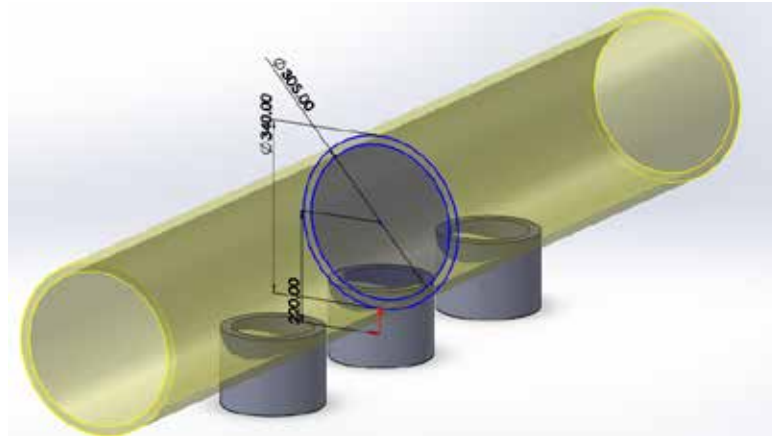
Croquis 2 y Extrusión 2, Manifold de Baja.
